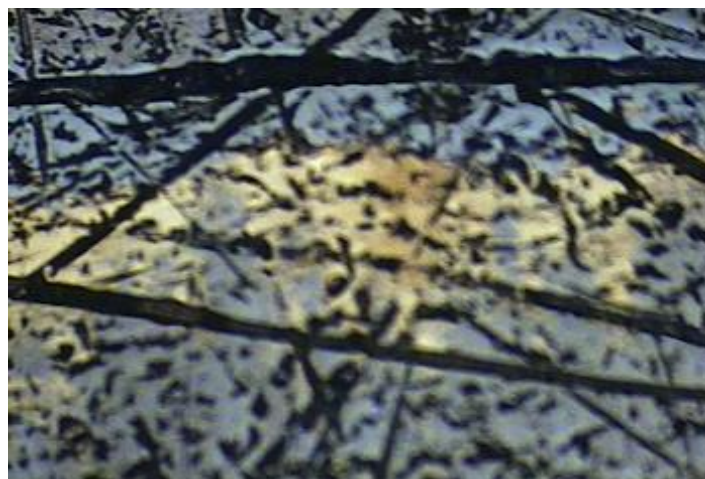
Поверхня деталі, на якій наведені послідовні ділянки «сталь-бронза» після наступної механічної обробки (риски на фото – сліди абразивних зерен)
